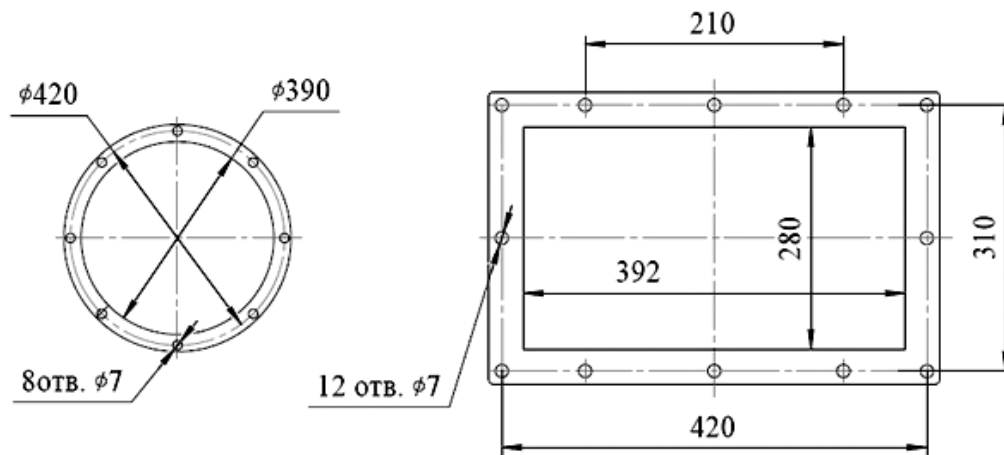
Вентиляторы ВРП-115-49-5,6. Присоединительные размеры
